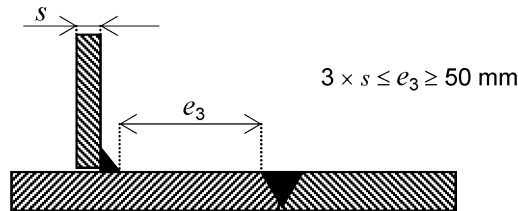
Abstand zwischen den Nahrändern von Schweißverbindungen
